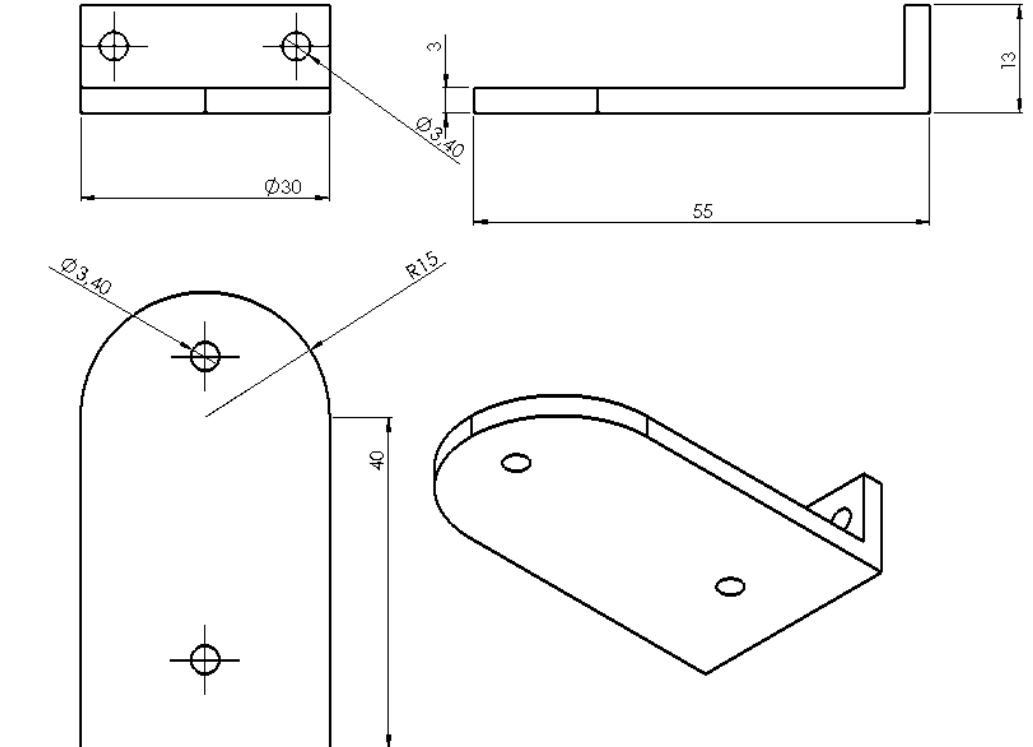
Pleksiglas malzemedan yapılan alt tabla.
